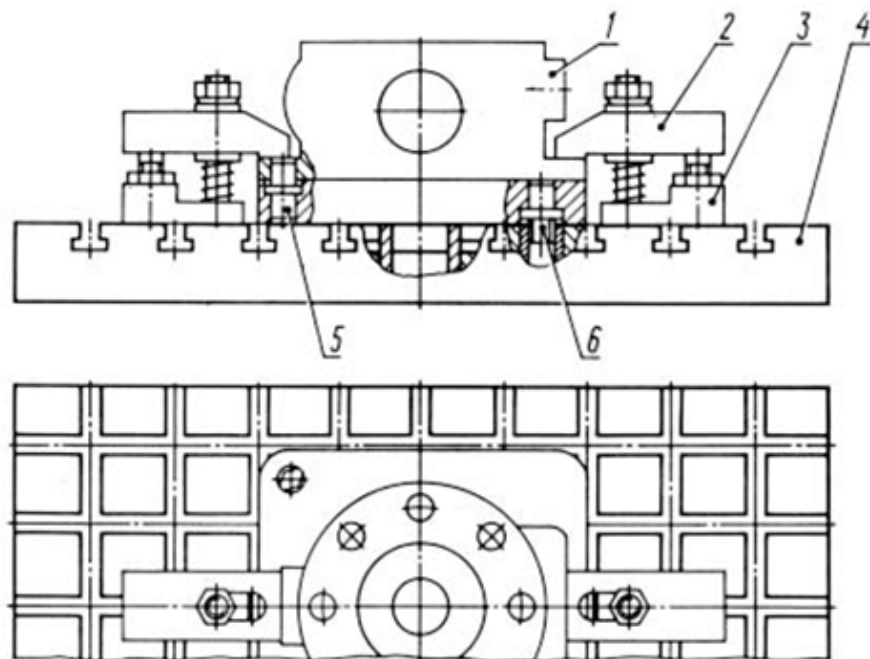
Пристрій з урахуванням координатної плити: 1 – заготовка; 2 – прихоплювач; 3 – опора; 4 - плита
